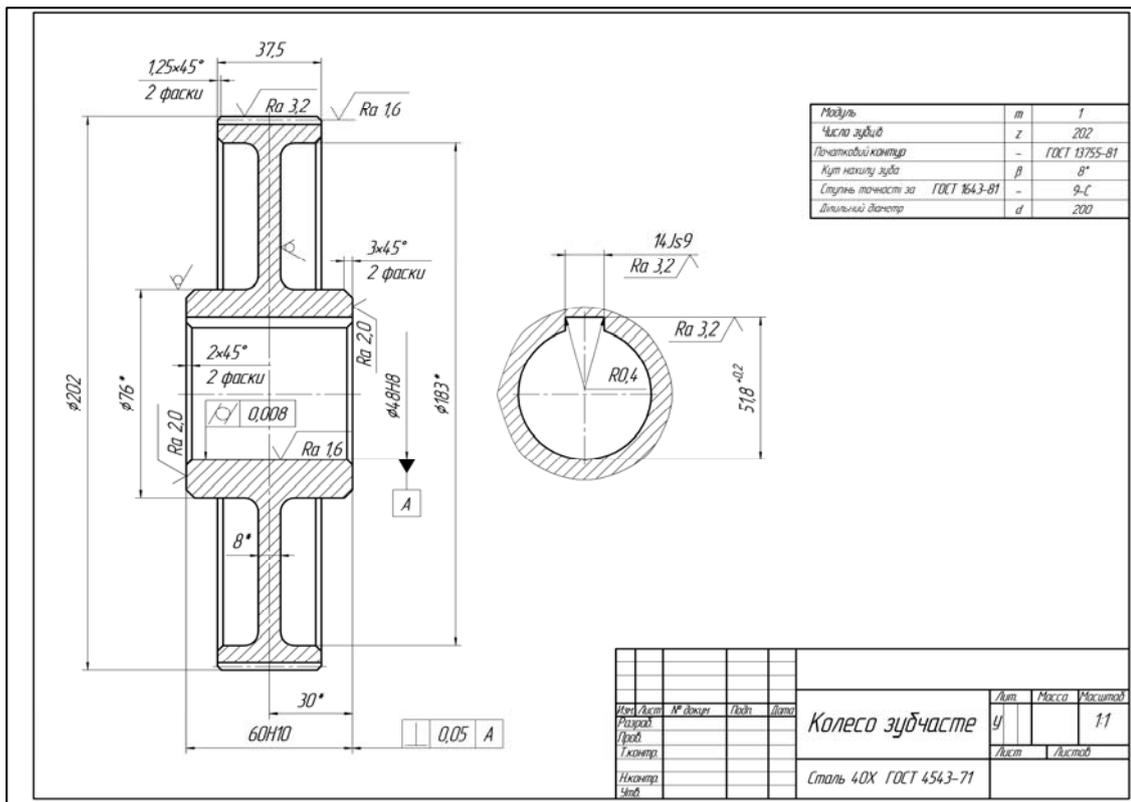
Зразок креслення циліндричного зубчастого колеса
